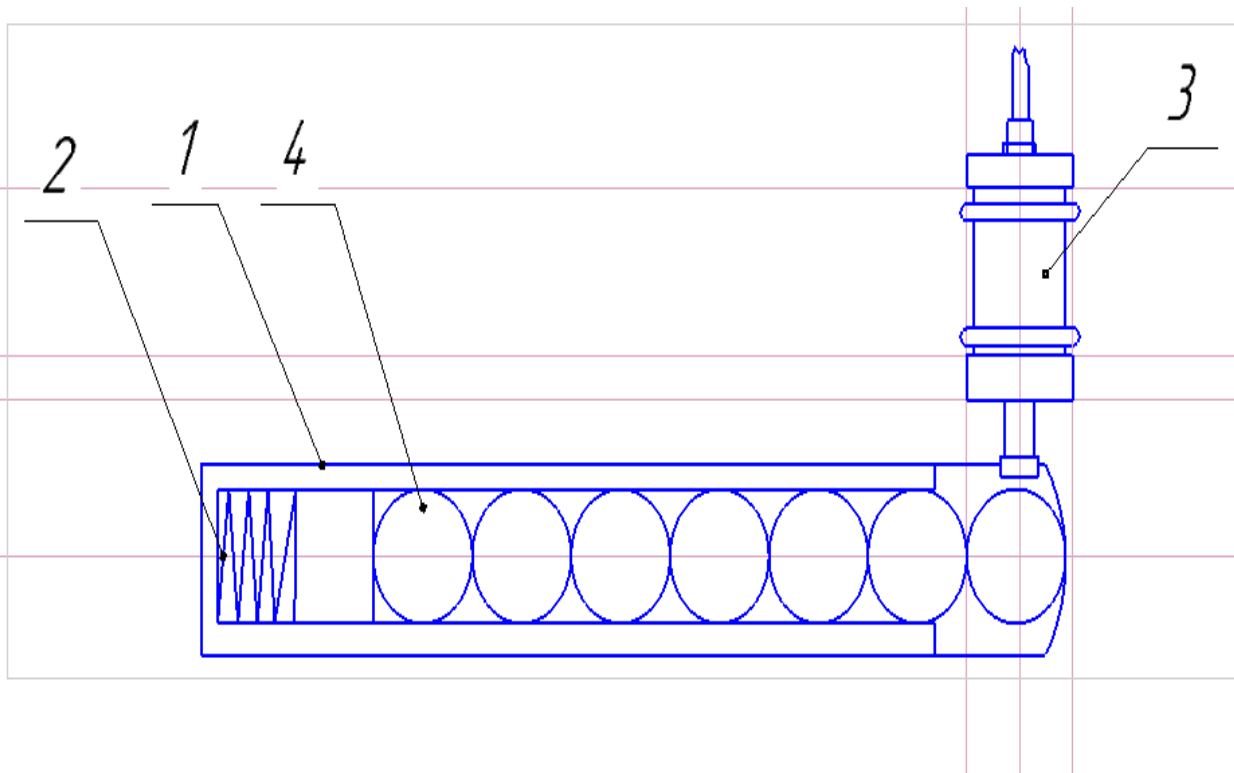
Пневматичний заряджальний апарат: 1-касета; 2-пружина з подавачем; 3-пневоциліндр односторонньої дії; 4-зразки
